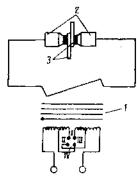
Принципиальная схема контактного нагрева: I— нагревательный траисформатор, 2— электроды, 3— деталя
